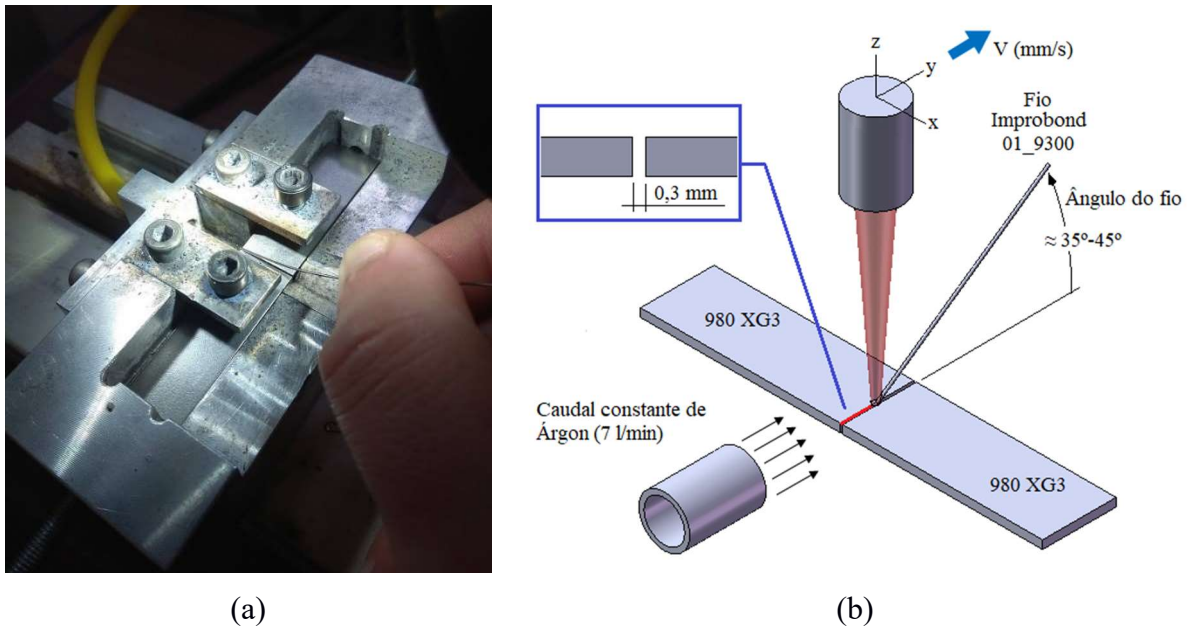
(a) alimentação manual de fio. (b) Esquema representativo da soldadura com metal de adição
